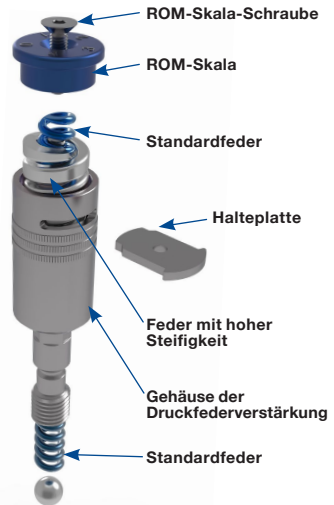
Entfernen Sie die Halteplatte und richten Sie die gewünschte Federkonfiguration ein.
